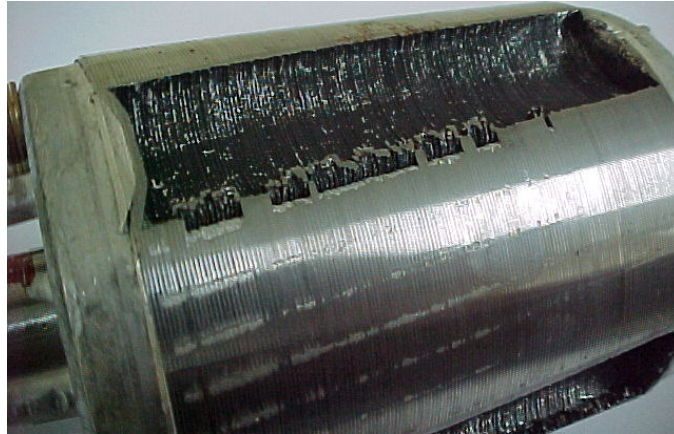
Rotor do projeto 4 – falhas na usinagem
